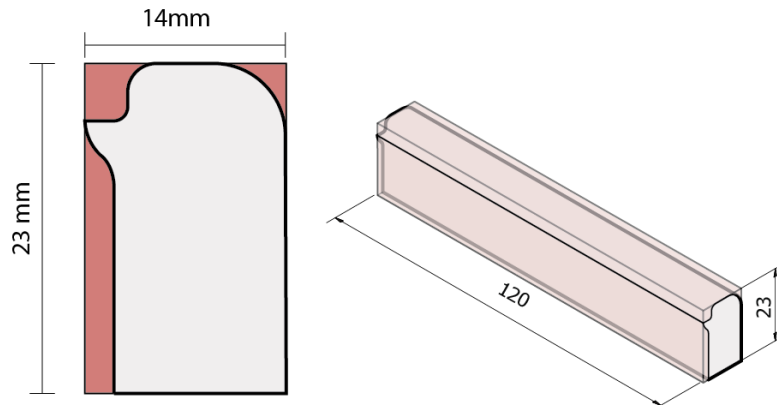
Dimensiones y desbaste del apoyo generador de paredes para corte en plancha de grilon
